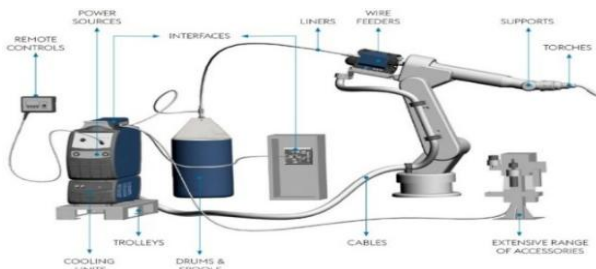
1 Welding Robot MIG OTC FD V6 500A
